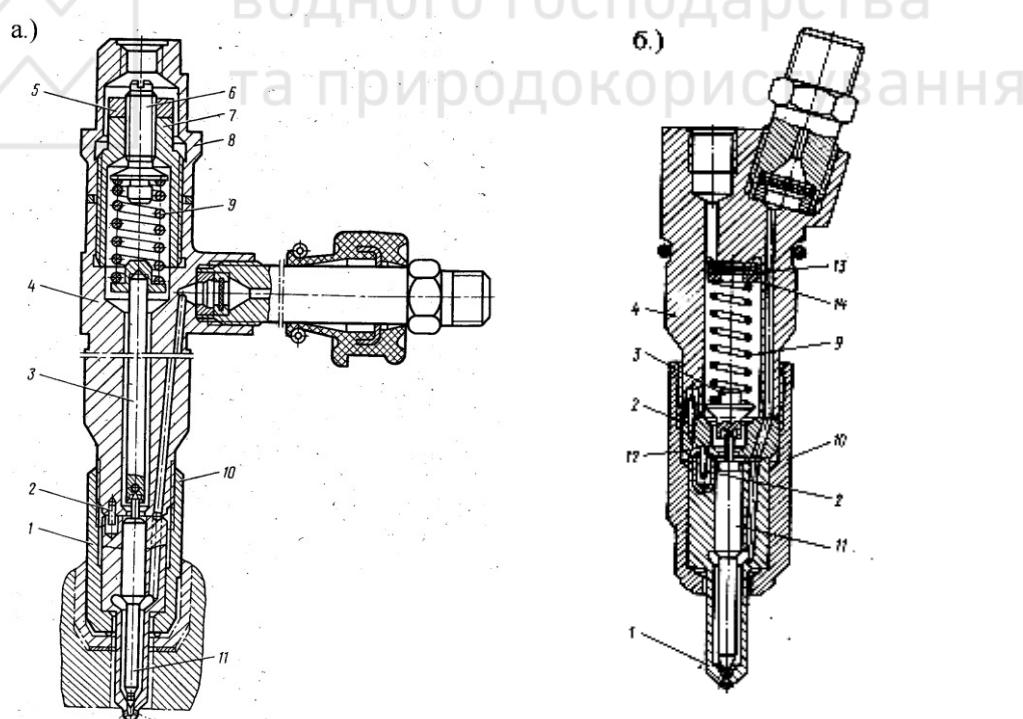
Форсунка: а) 1 – розпилювач; 2 – штифт; 3 - штанга; 4 – корпус форсунки; 5 – контргайка; 6 – регулювальний гвинт пружини; 7 – гайка; 8 – ковпачок; 9 – пружина; 10 – гайка розпилювача; 11 – голка розпилювача; 12 – проставка; 13 – регулювальні шайби; 14 – опорна шайба.
